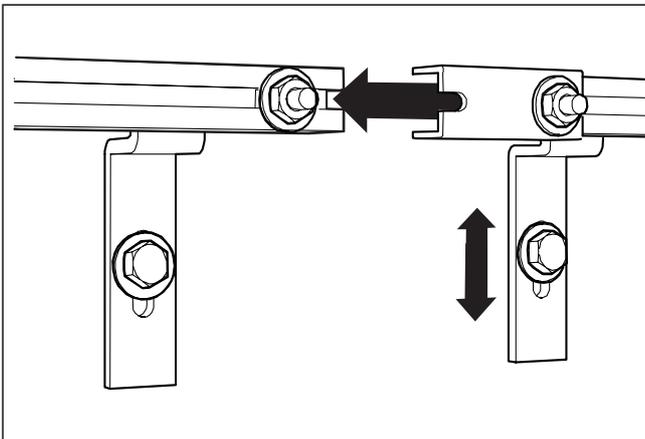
Болт М 10х20 с шайбой и гайкой вставить в уже смонтированную шину. Новую шину протянуть через головки болтов и вместе с соединительной деталью задвинуть до упора на предварительно смонтированную шину. Затянуть болт.
